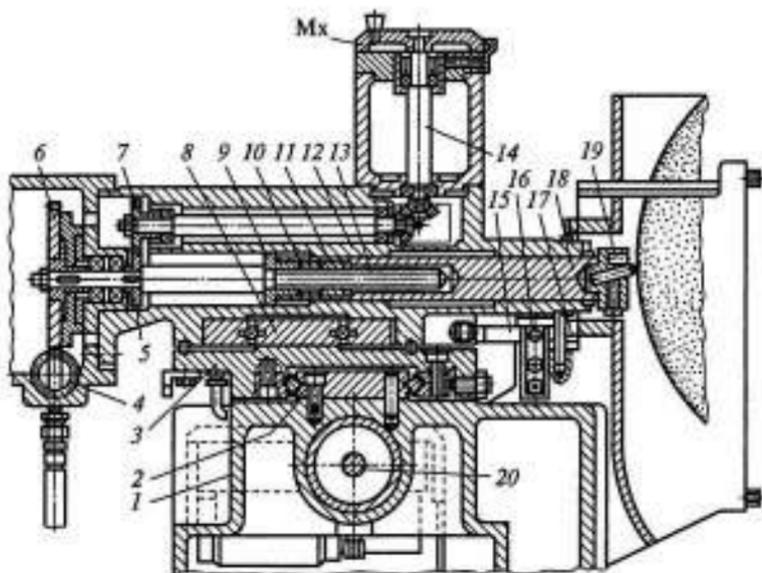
Устройство автоматической правки шлифовального круга:
